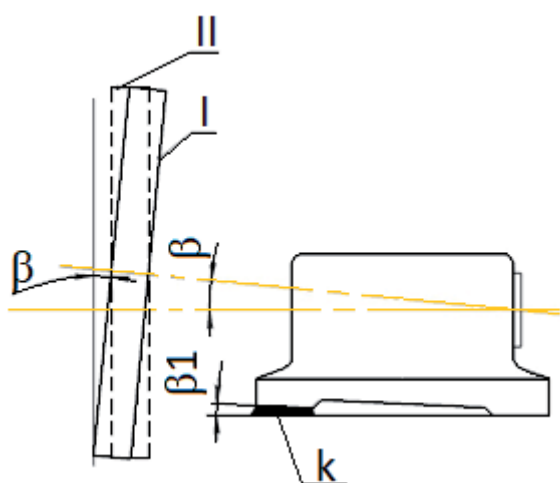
Схема регулировки положения корпус электродвигателя – станина
